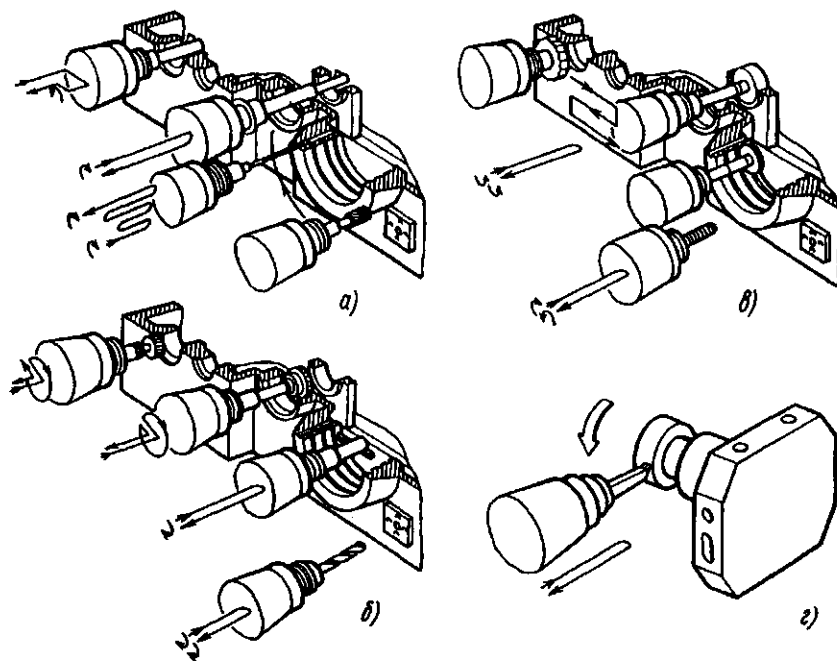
Виды обработки, выполняемые на токарно-сверлильно-фрезерно-расточном станке мод. "Модуль ИР320ПМФ4": а – обратное цевкование, растачивание, сверление глубоких отверстий, фрезерование; б – фрезерование по контуру, растачивание канавок, сверление; в – фрезерование плоскостей, обработка отверстий, канавок, нарезание резьбы; г – токарная обработка с вращением закрепленной на палете заготовки
